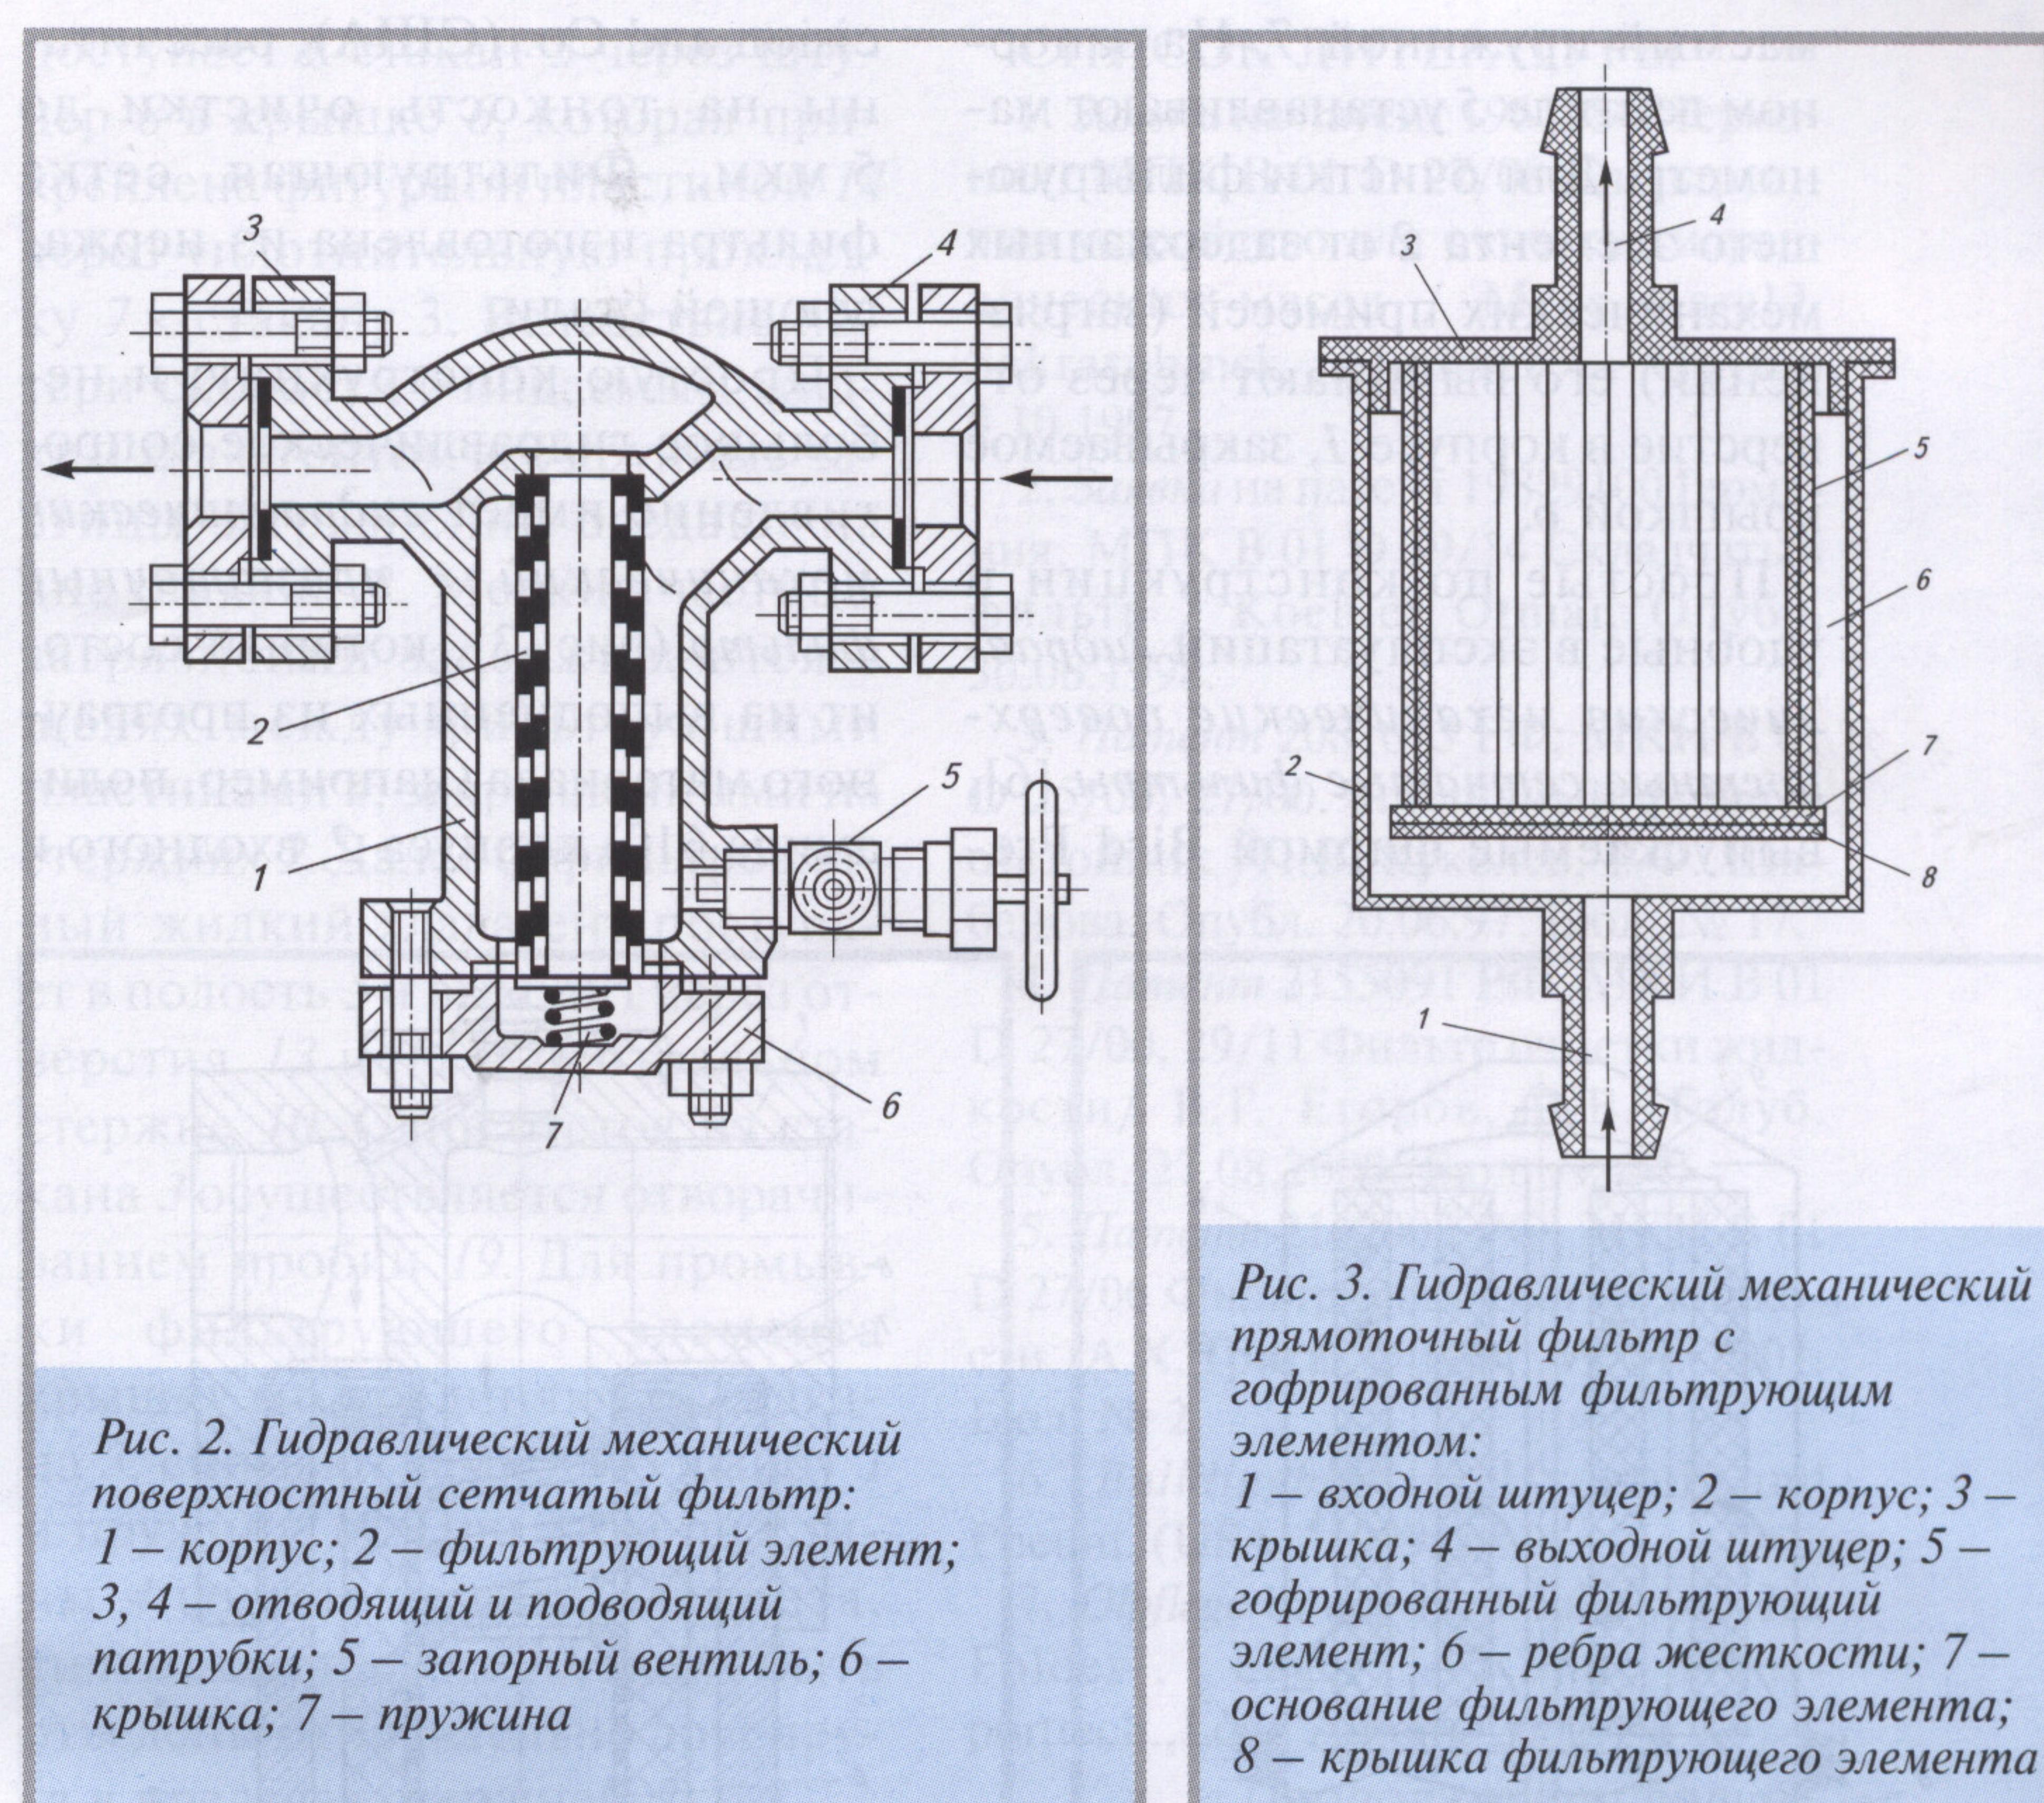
Гидравлический механический поверхностный сетчатый фильтр:
